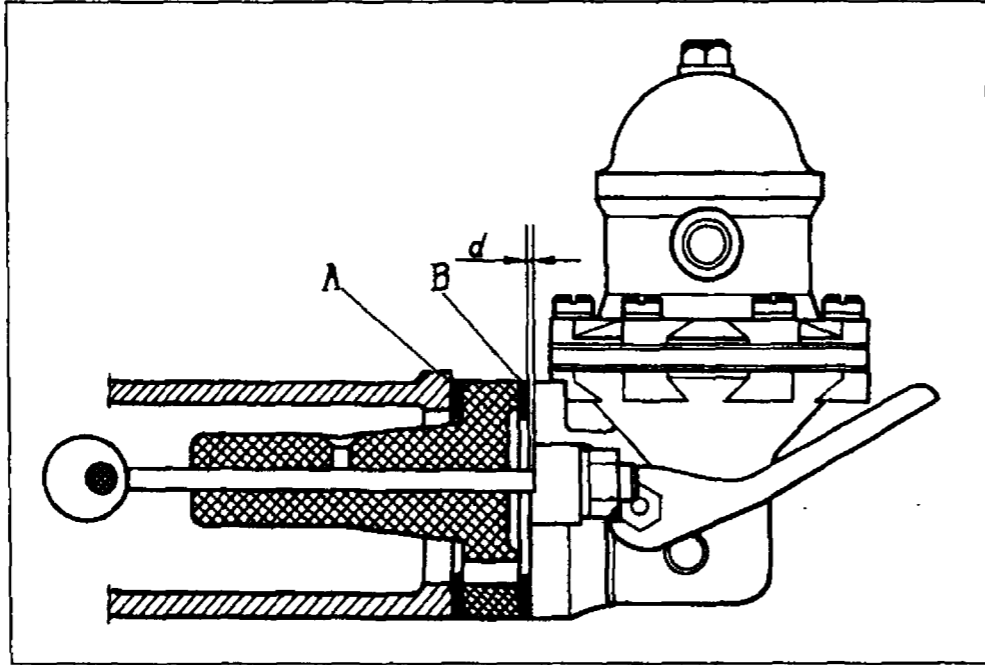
Схема контроля и регулировки выступающего толкателя привода насоса:
